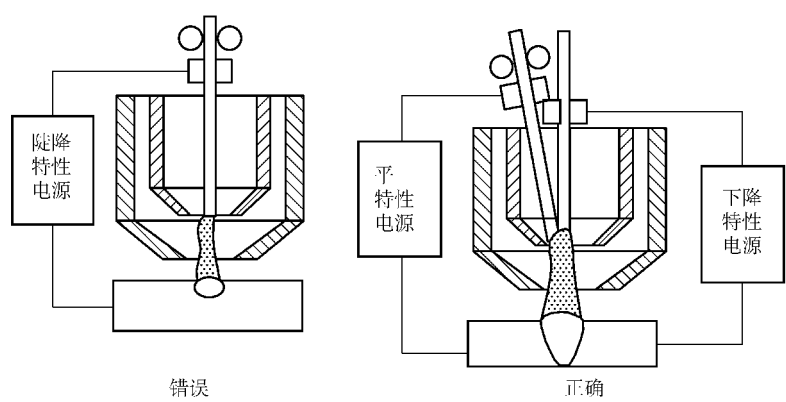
熔化极等离子弧焊的结构示意图
